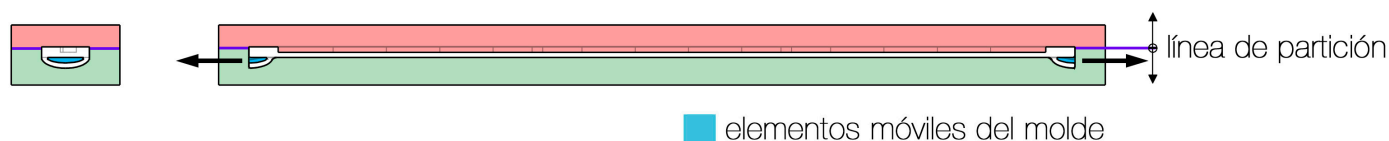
mitades molde pieza “8.6.3.- Tapa filtro”
